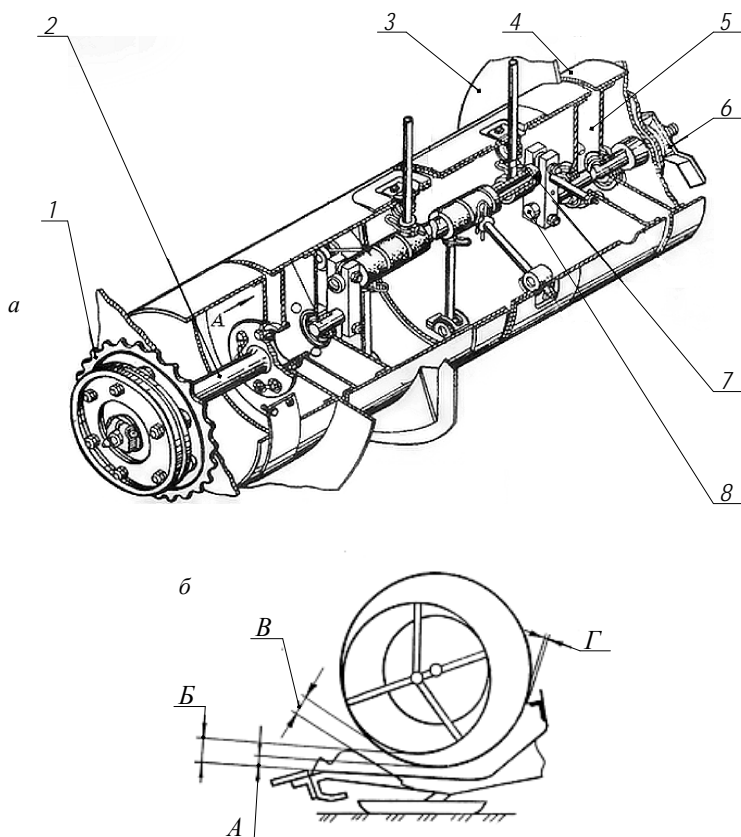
Конструктивная схема и основные регулировки шнека жатки:
